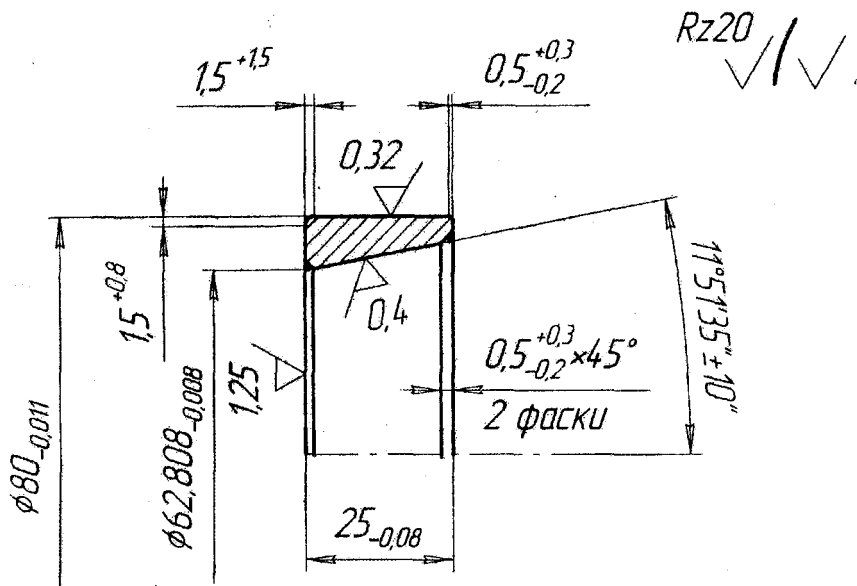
Чертеж заготовки наружного кольца подшипника 6-7607AY
